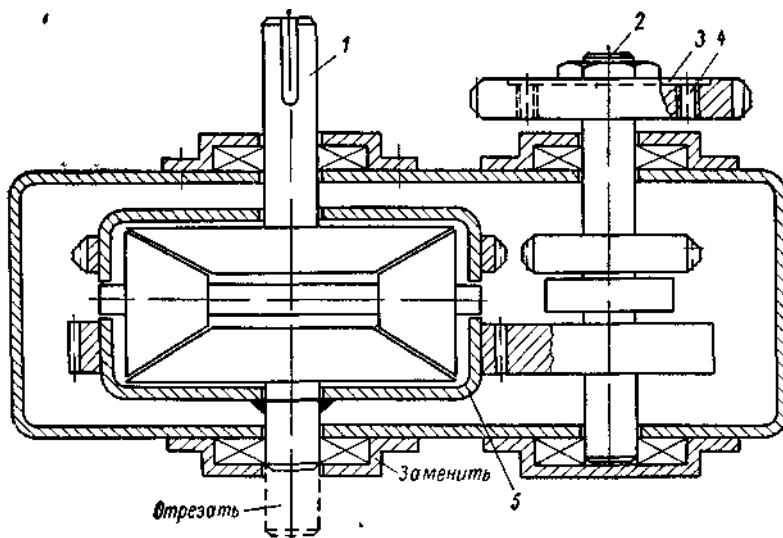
Схема переделки дифференциала в редуктор с реверсивным устройством.
